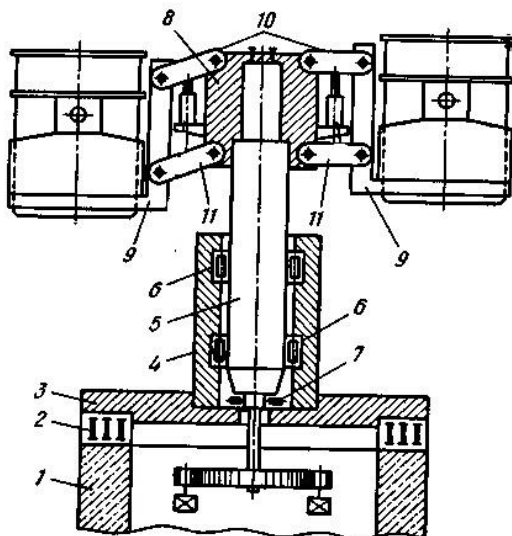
Сталерозливний стенд конструкції ВНДІМетмаш
